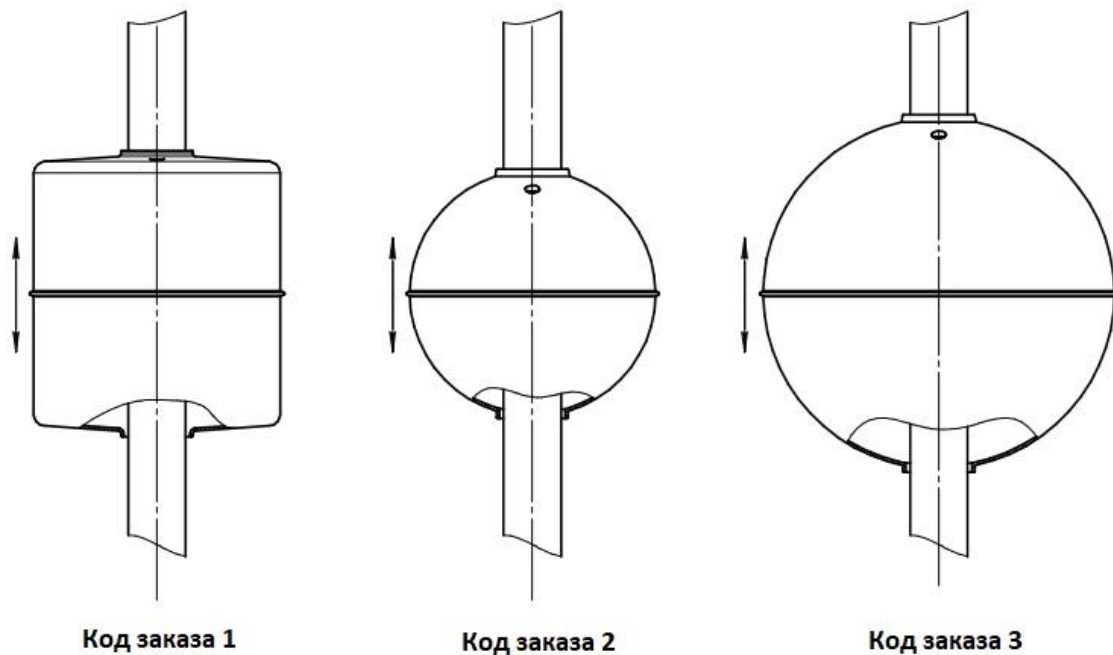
Монтажная часть ЭЛЕМЕР-УПП-11 с различными типами поплавков.
